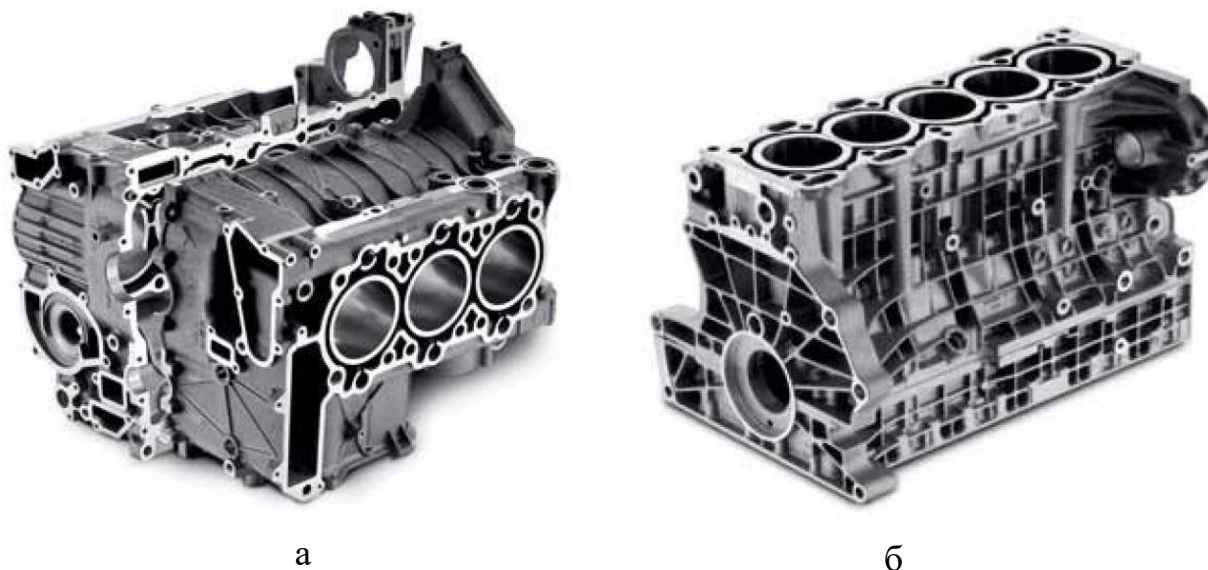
Блоки циліндрів конструкції типу «Open-Deck» [21]
